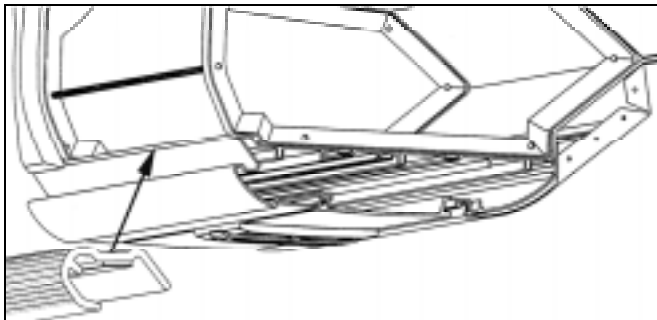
Porte-colis de type ouvert. Emplacement de la moulure à poser.
